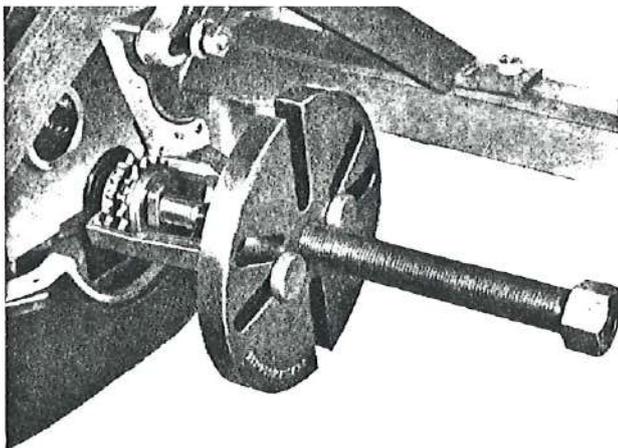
Desmontaje del piñón mando distribución, mediante el extractor A. 6004 provisto de la brida A. 40000.
